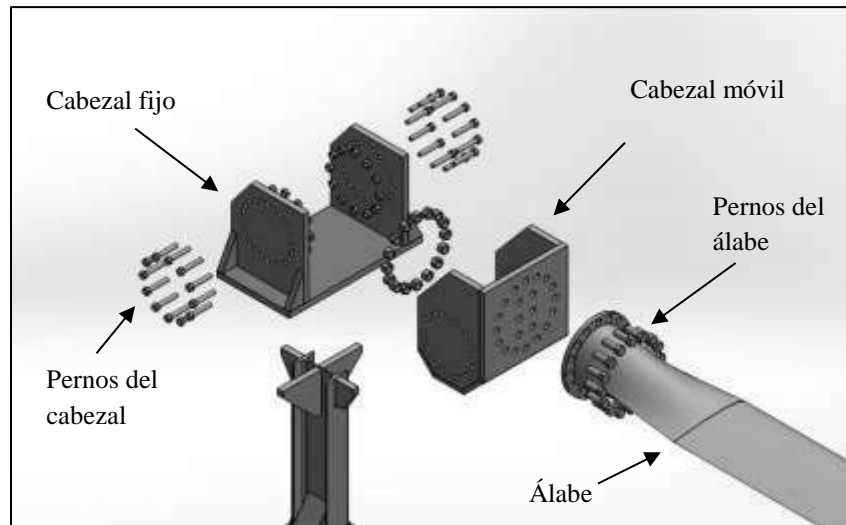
Vista explosionada del cabezal 1. Fuente: SOLIDWORKS 2017.
